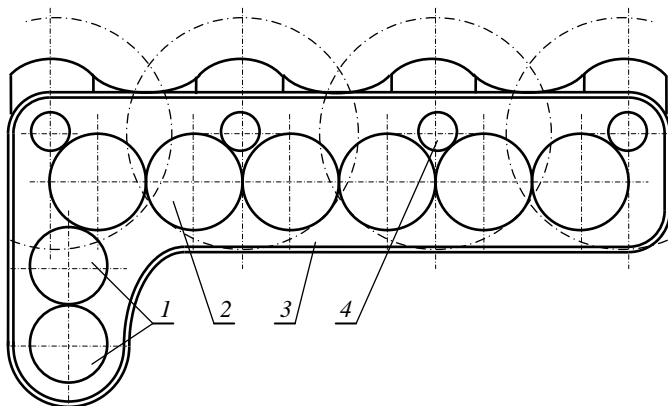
Схема привода роторов рабочего органа косилок Claas и Krone: 1 – приводные шестерни; 2 – ведущие колеса; 3 – корпус; 4 – роторы
